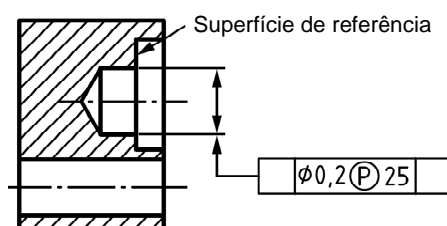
Superfície de referência do elemento toleranciado projetado (ISO/DIS 1101.2)
